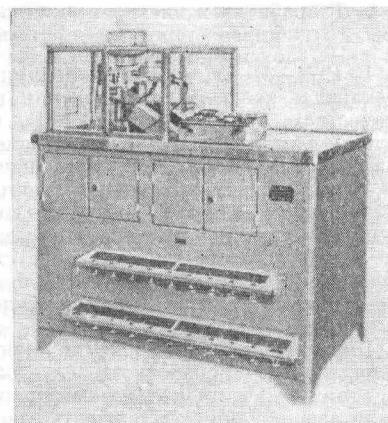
Автомат для сортировки роликов подшипников на 40 групп через 1 мкм.
